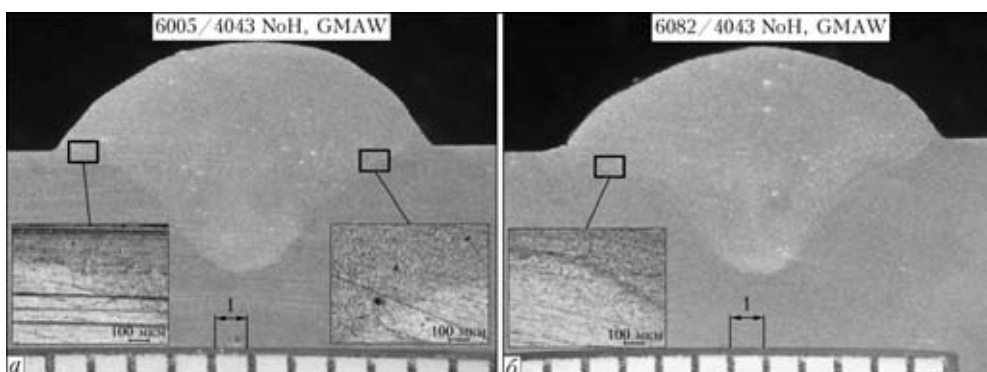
Макрошлифы соединений сплава 6005 (а) и 6082 (б), выполненных с использованием присадочного металла 4043 без предварительного подогрева способом GMAW
